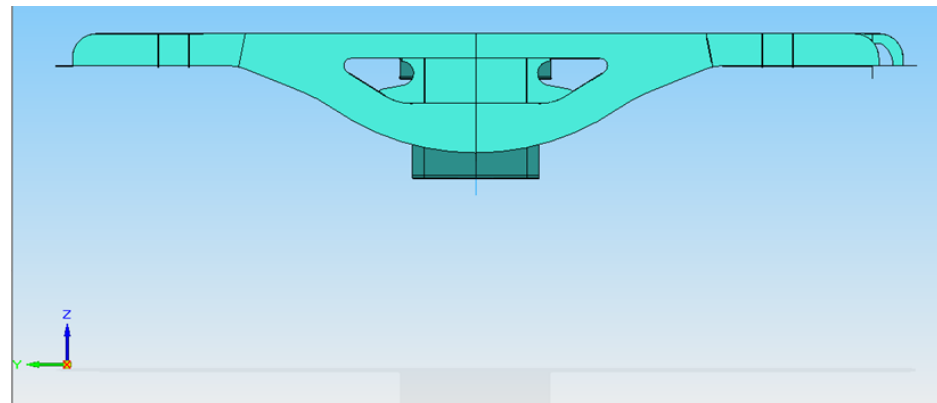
Conjunto de bastidor. Vista: Planta
